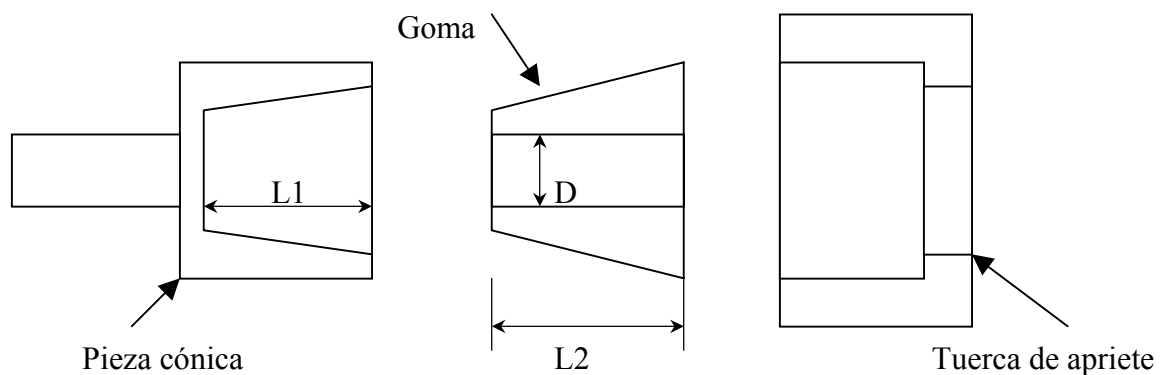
Partes que componen la pinza de sujeción.
